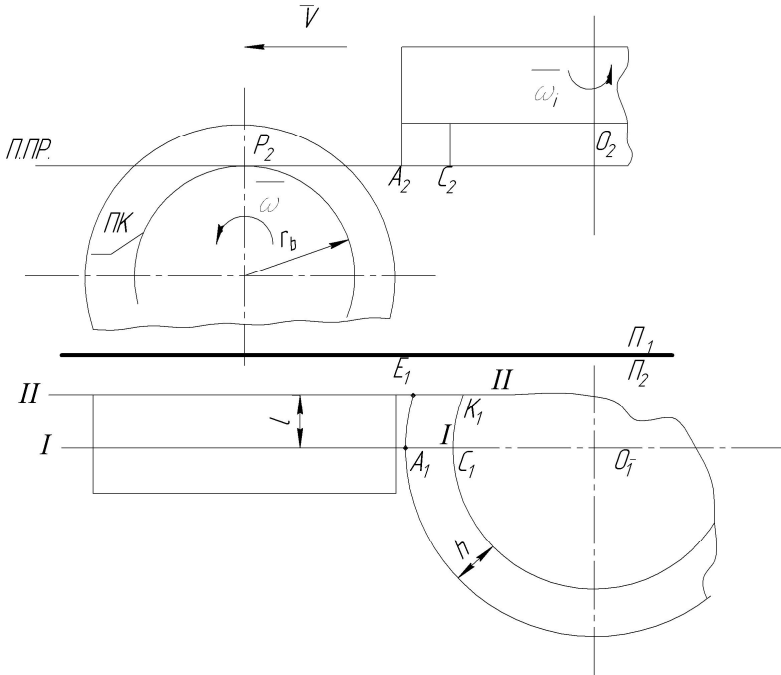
Схема оброблення зубчастих коліс профілюючими колами торцевої фрези
